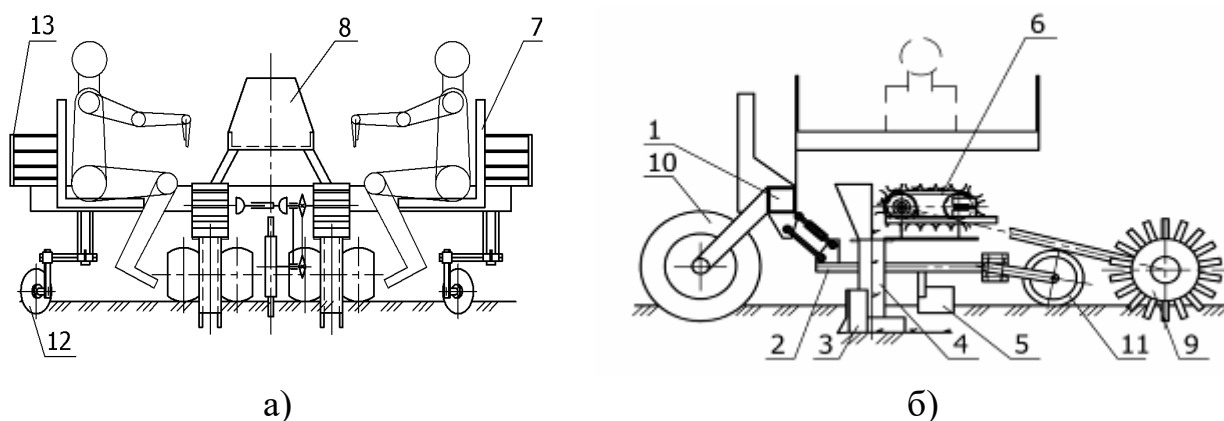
Схема дворядної садильної машини СМ-2 (розробка ІБКіЦБ [80]):
